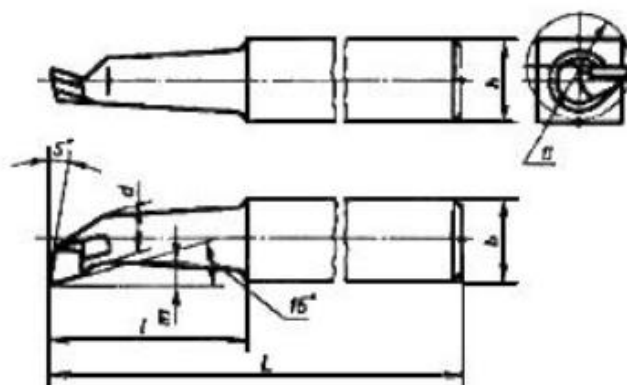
Резец 2140-0030 T15K6 ГОСТ 18879-73
